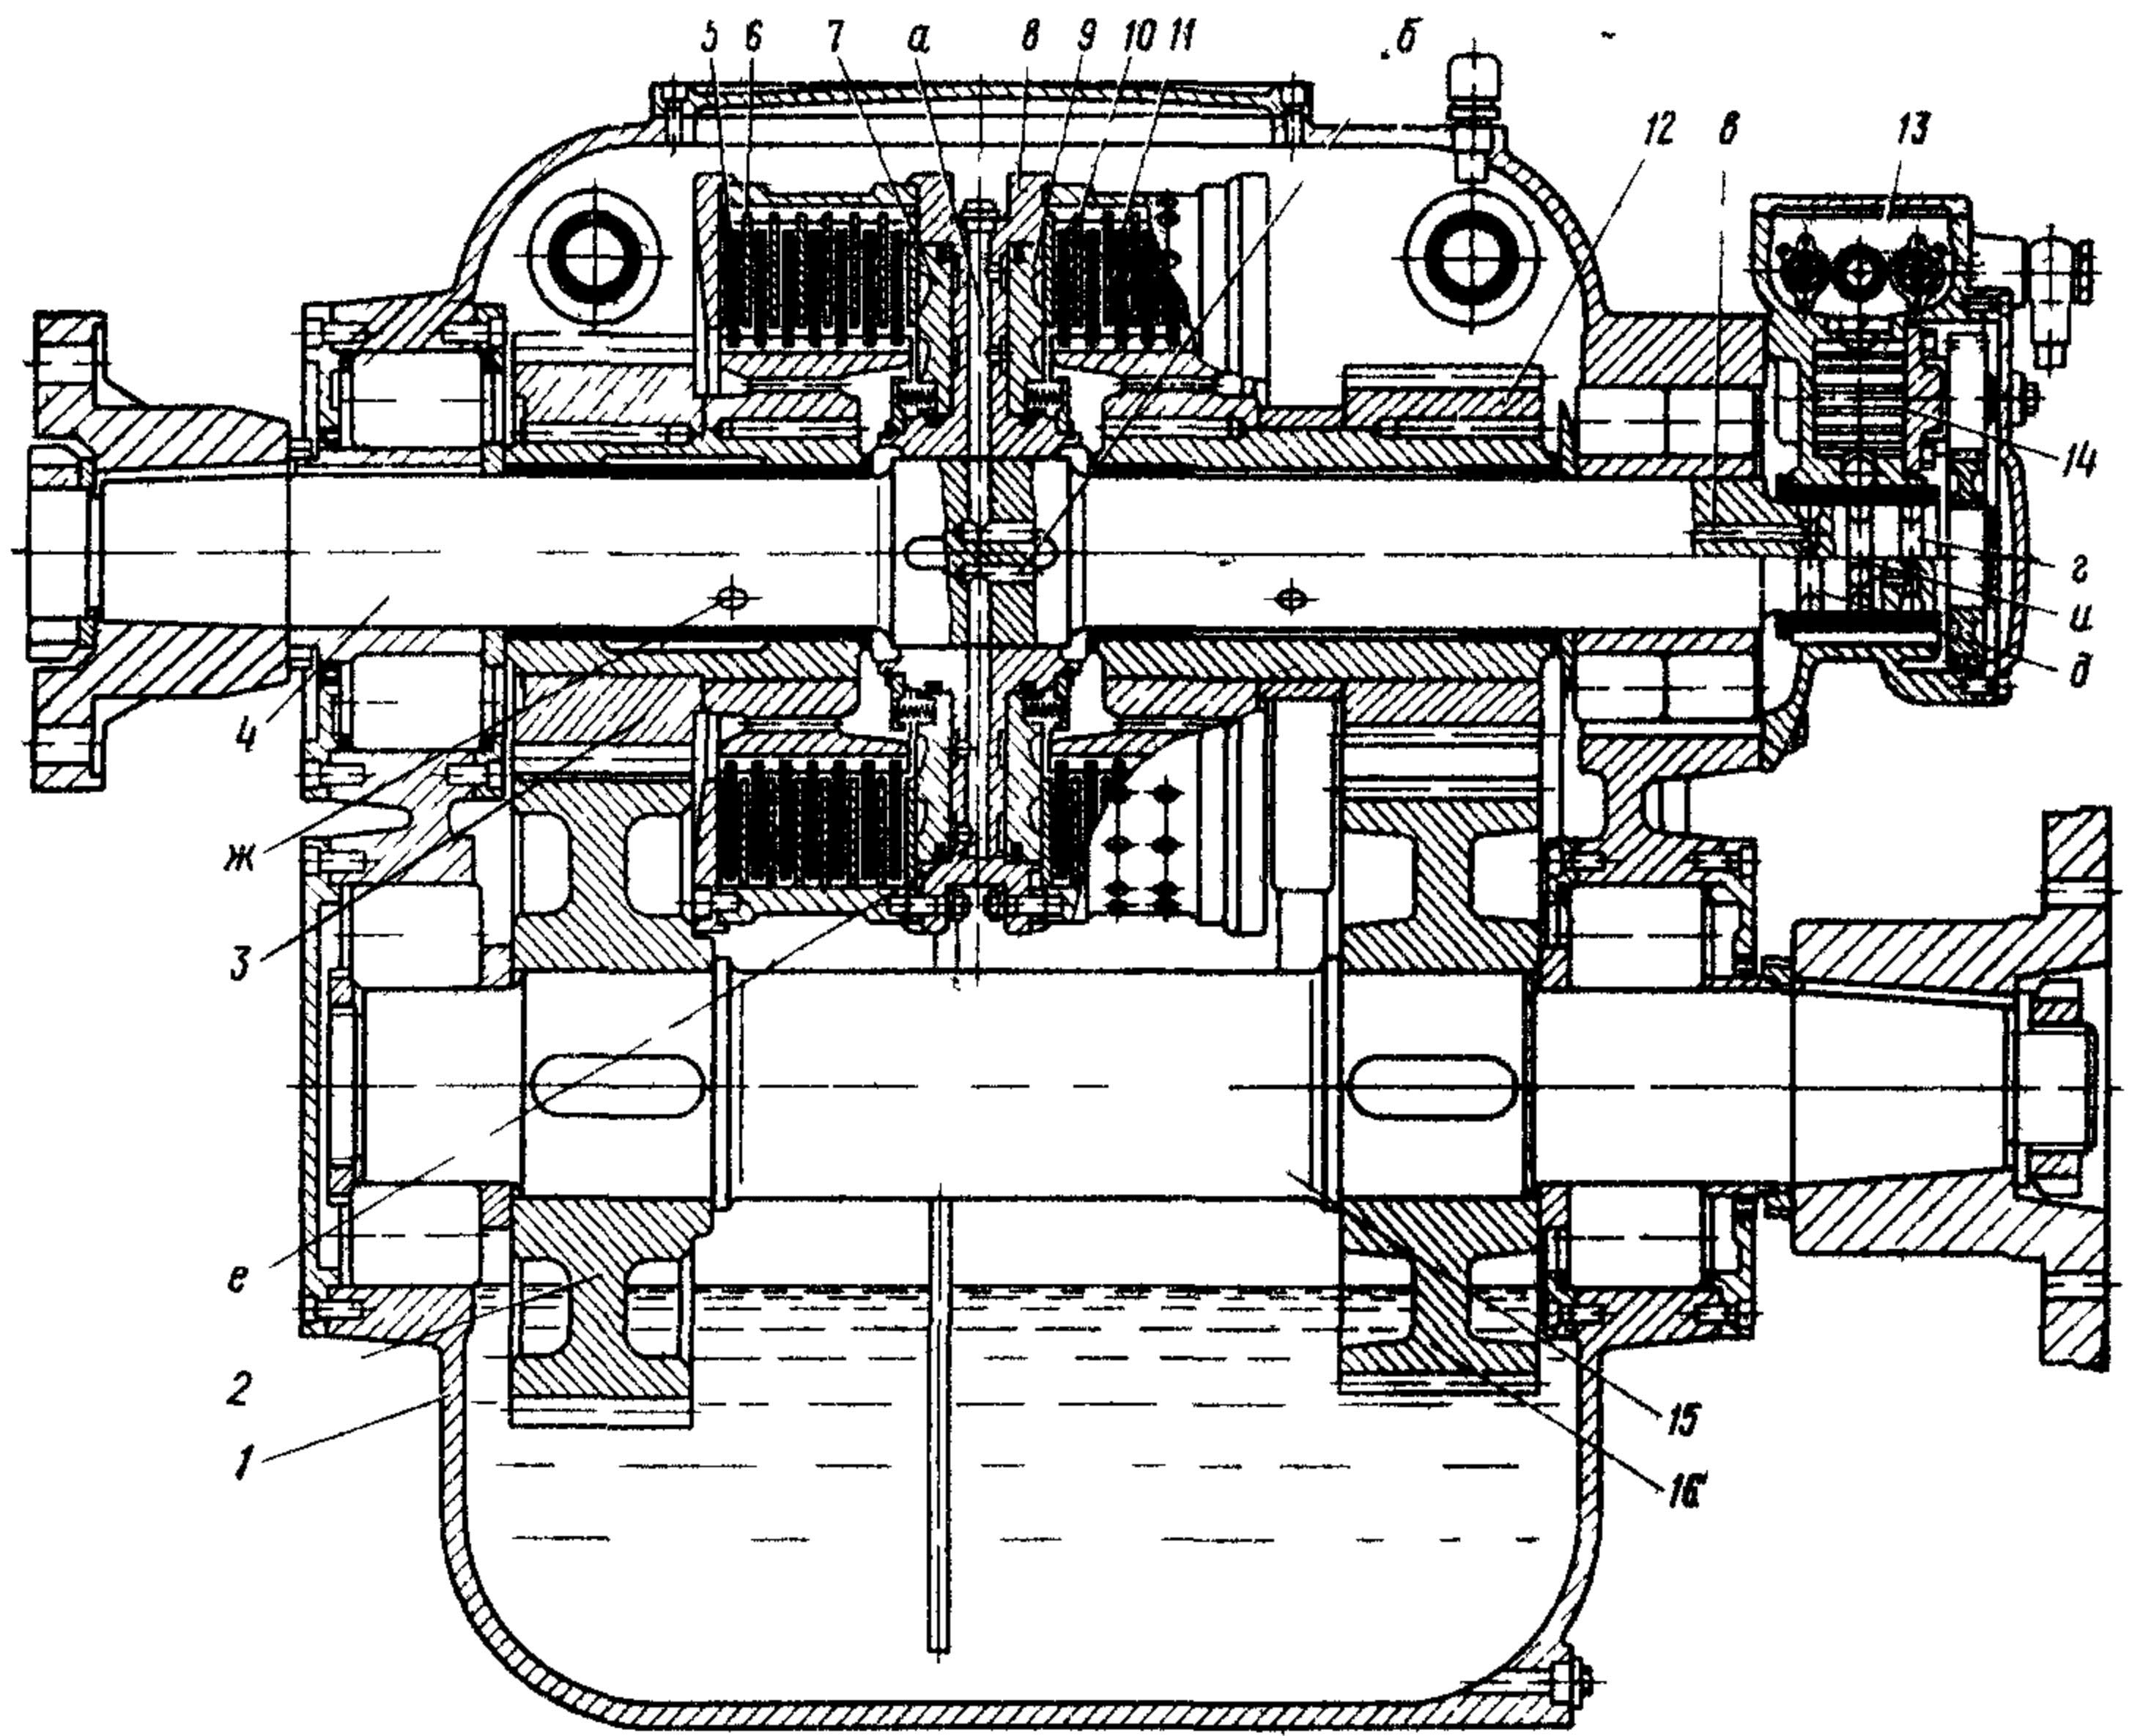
Ревёрс редуктор двигателя 6Л275ПН
